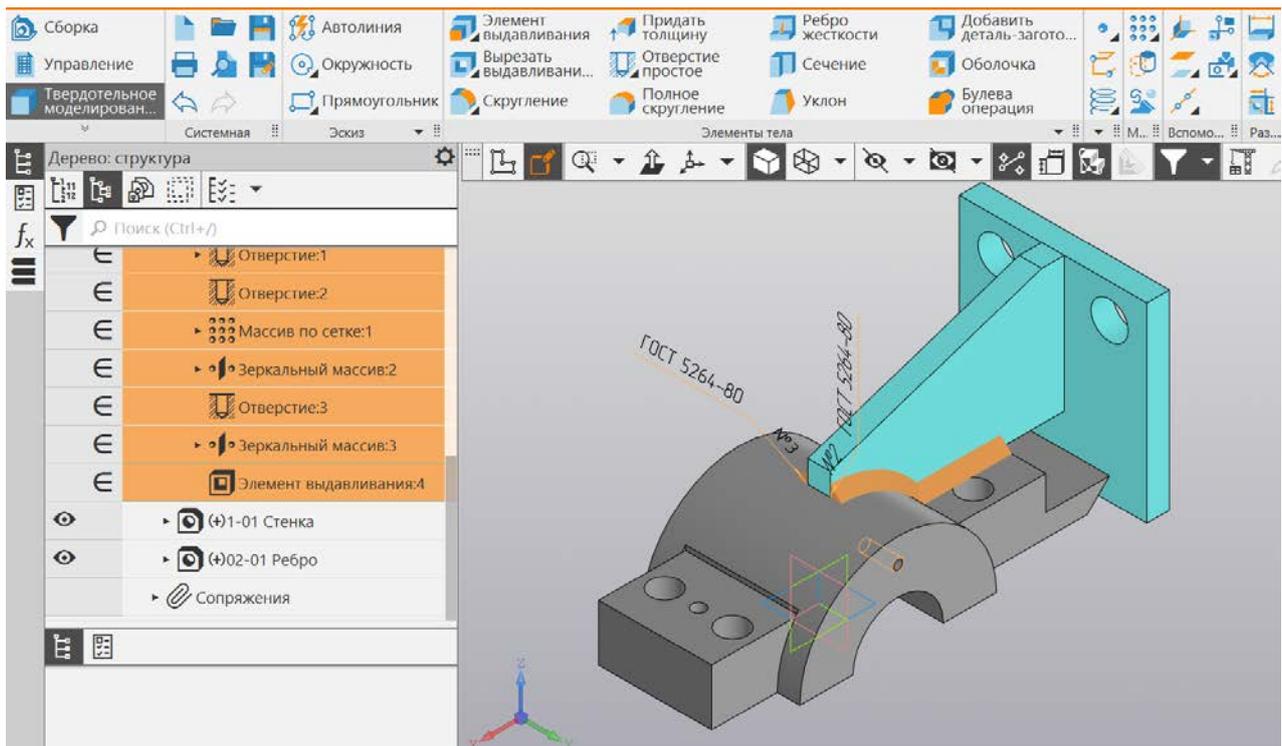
Опора с подготовленной кромкой под сварку
